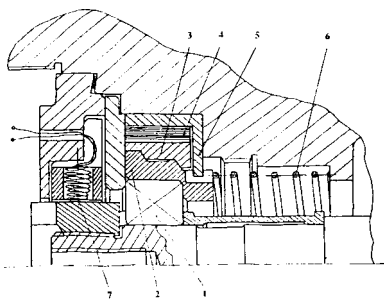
Общий вид узла с исследуемой упругодемпферной опорой с демпфером многослойного типа: 1-подшипник; 2 - втулка; 3 - втулка, разрезанная на сегменты; 4 - демпфер; 5 -корпус демпфера; 6 - пружина; 7 - датчики перемещений.
